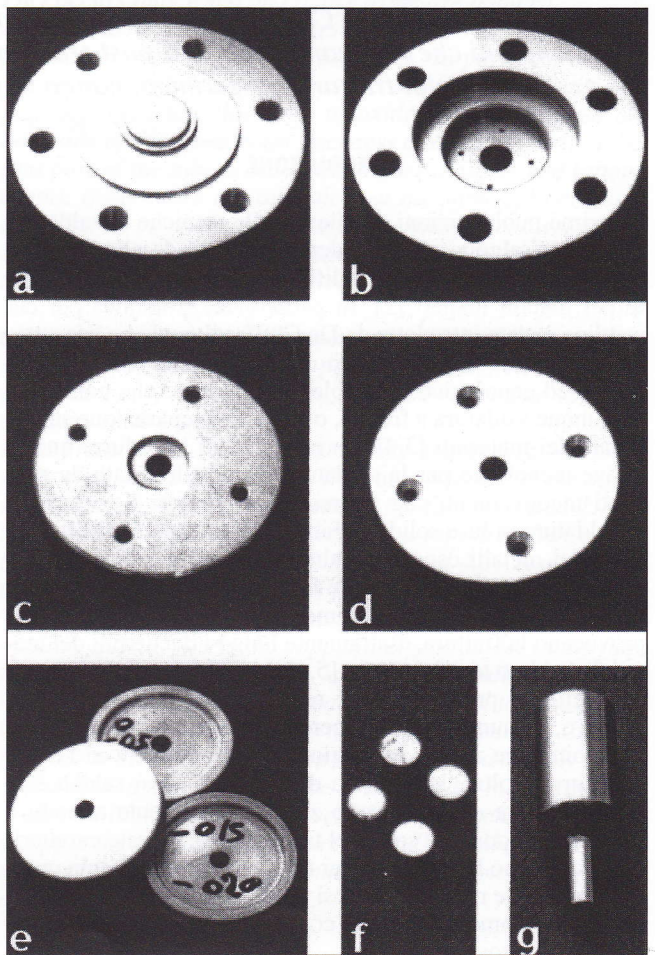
Componenti principali del sistema di saldatura a freddo per cut welding utilizzato per il presente studio. a) base del dispositivo con il sistema di fissaggio del campione di Al, b) parte superiore, c) adattatore con scanalature per alloggiare il rame asportato dal tagliente, d) tagliente, e) disco di alluminio, f) cilindretti di Cu, g) punzone.
